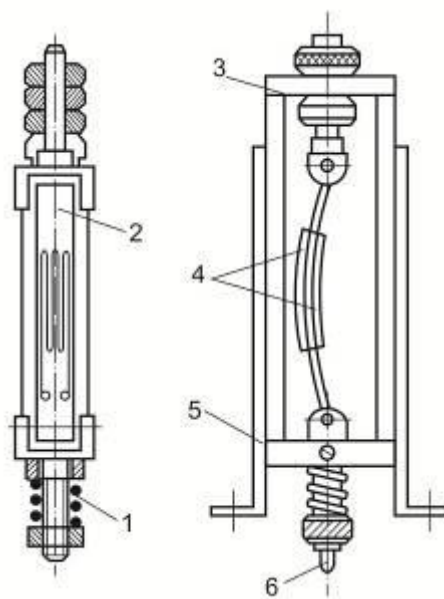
Устройство для измерения износа с помощью преобразователя сопротивления: 1 - пружина; 2 - упругая балочка; 3 - корпус; 4 - тензодатчики; 5 - угольники; 6 - щуп.
